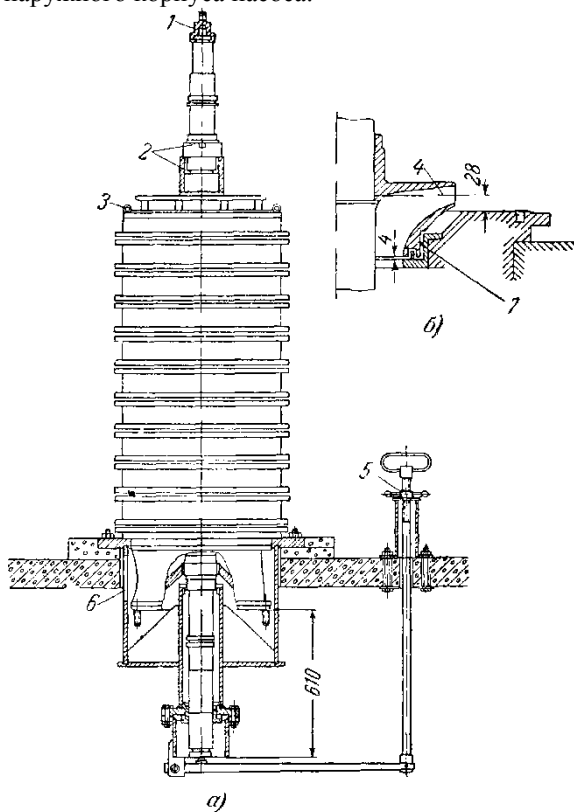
Приспособление для выемки внутреннего корпуса питательного насоса ПЭ-430-220.
